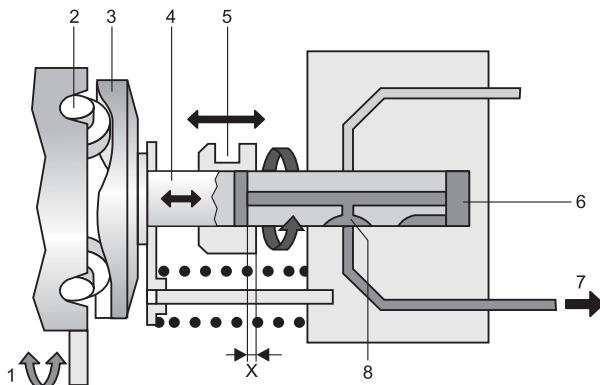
Система впрыска с распределительным аксиальным ТНВД: 1 — траектория поворота роликового кольца; 2 — ролик; 3 — кулачковая шайба; 4 — аксиальный плунжер-распределитель; 5 — регулирующая втулка; 6 — камера высокого давления; 7 — подача топлива к форсунке; 8 — распределительный паз; X — активный ход плунжера
